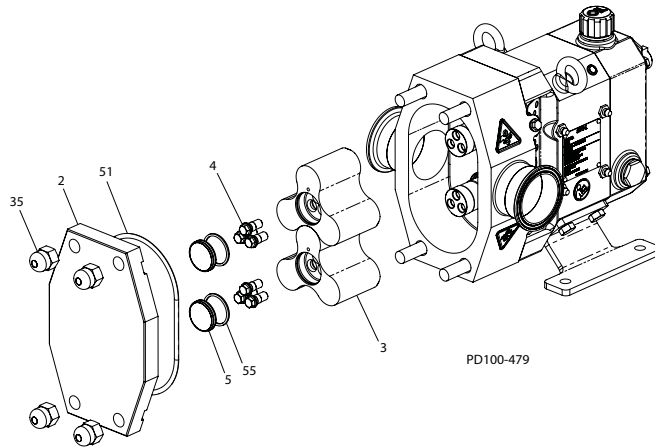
Desmontaje de la cubierta y del rotor de la bomba
